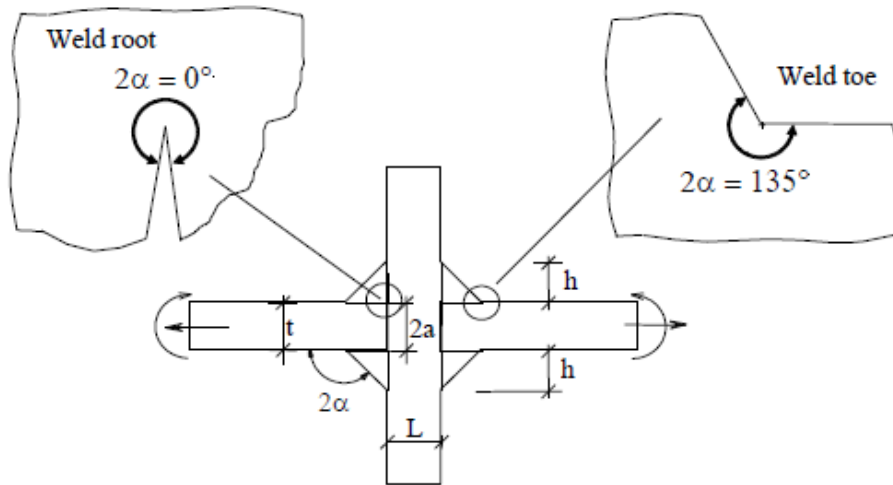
Giunto saldato con cordone di saldatura portante [5]
